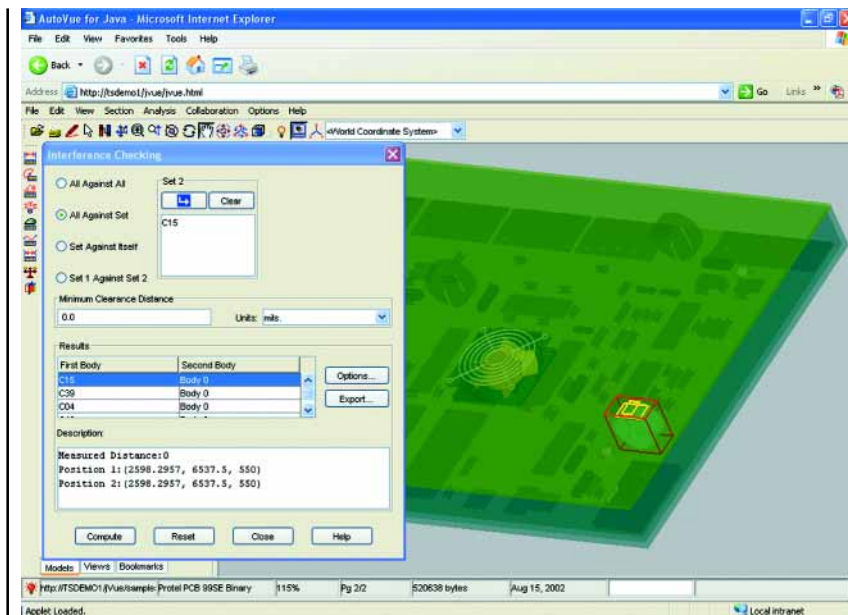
Интерфейс пользователя AutoVue для проверки наложений
